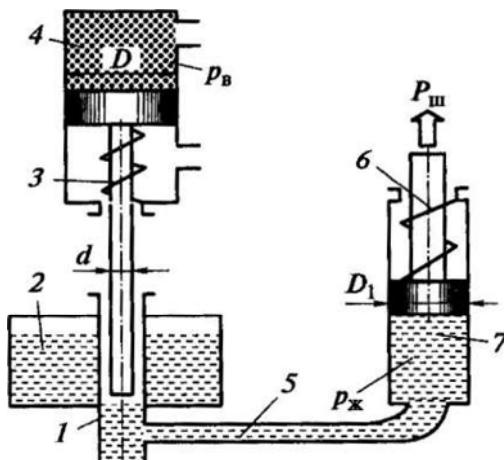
Схема пневмогидравлического преобразователя прямого действия: 1 а 7 — гидроцилиндры; 2 — резервуар; 3 и 6 — пружины; 4 — пневмоцилиндр; 5 — трубопровод выпуска отработавшего воздуха обратное движение поршней осу-
